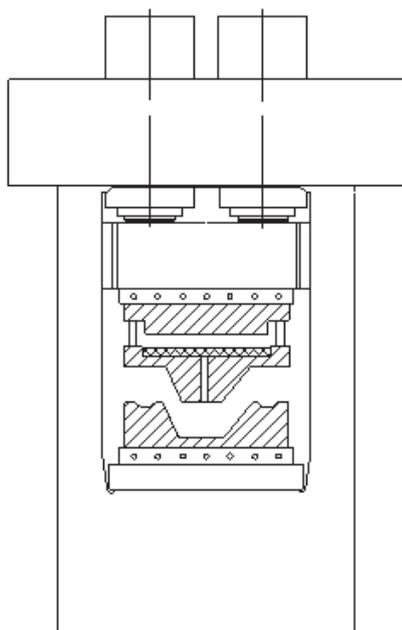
Presse zum Spritzpressen mit Formmasse im separaten Hohlraum
